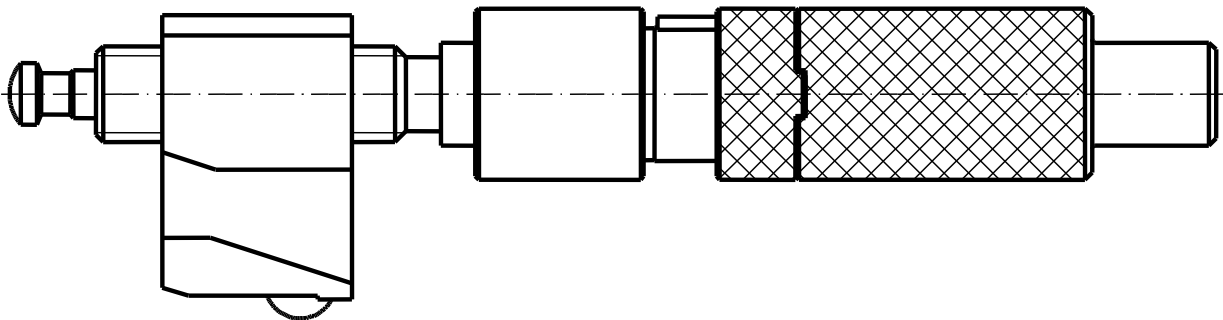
Zugschraubebaugruppe mit Hydraulikhilfe und Halter.
